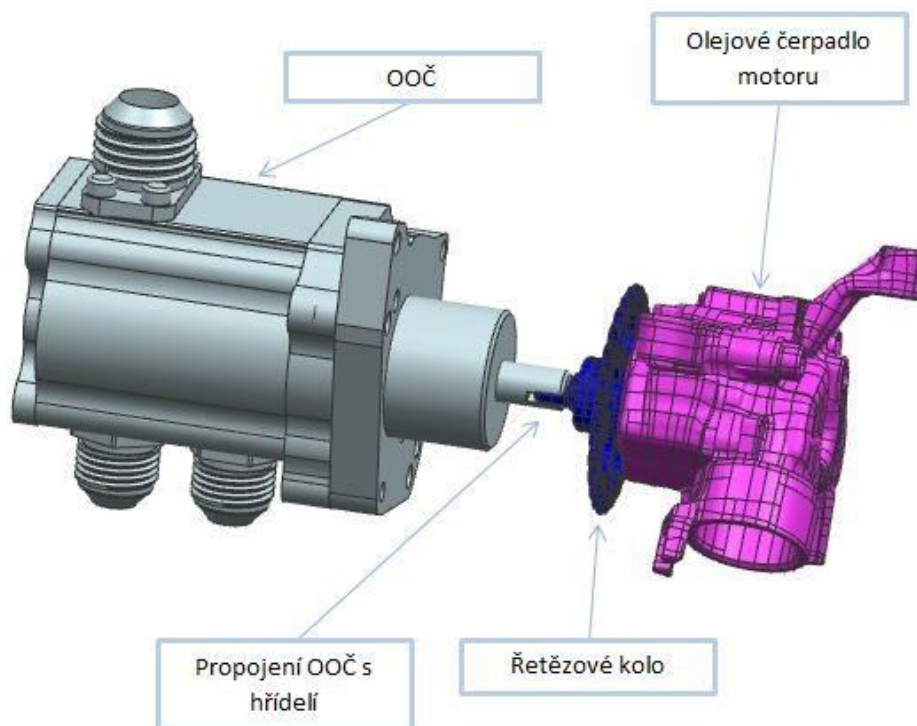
Popis částí OOČ od firmy Dailyengineering
